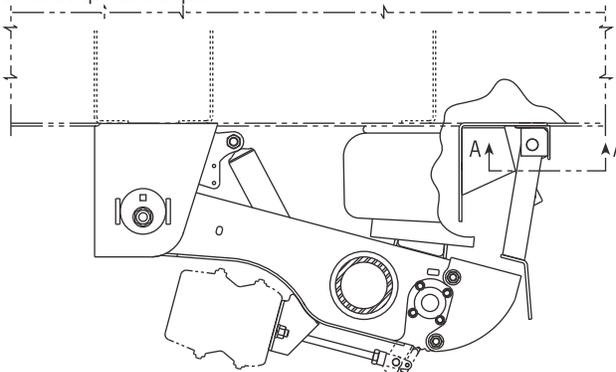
Detalles de soldadura del Kit SLKF
